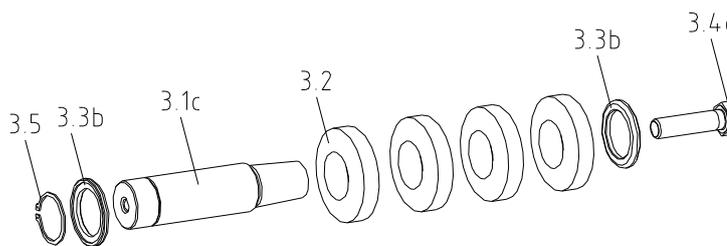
Bolzen KX-D AB komplett (Ausf. B)
